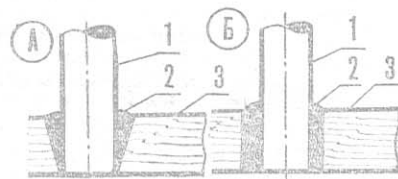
Схема крепления направляющих трубок (А — первой, Б — второй):
